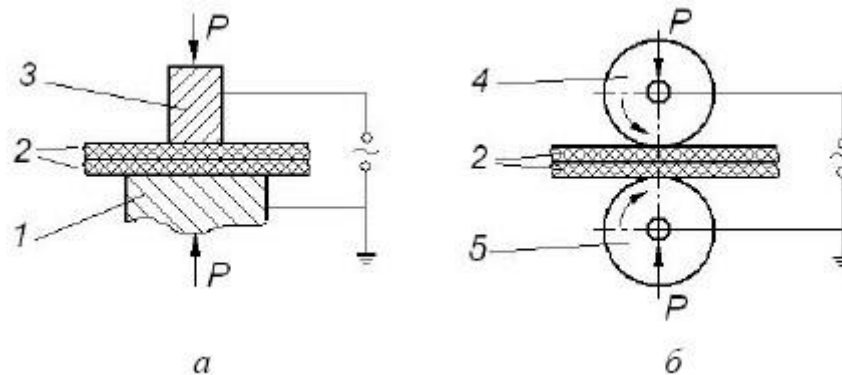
Прессовая (а) и роликовая (б) высокочастотная сварка пластмасс: 1 – заземленная обкладка конденсатора; 2 – свариваемый материал; 3 – высокопотенциальный электрод; 4 - высокопотенциальный ролик; 5 - низкопотенциальный ролик
